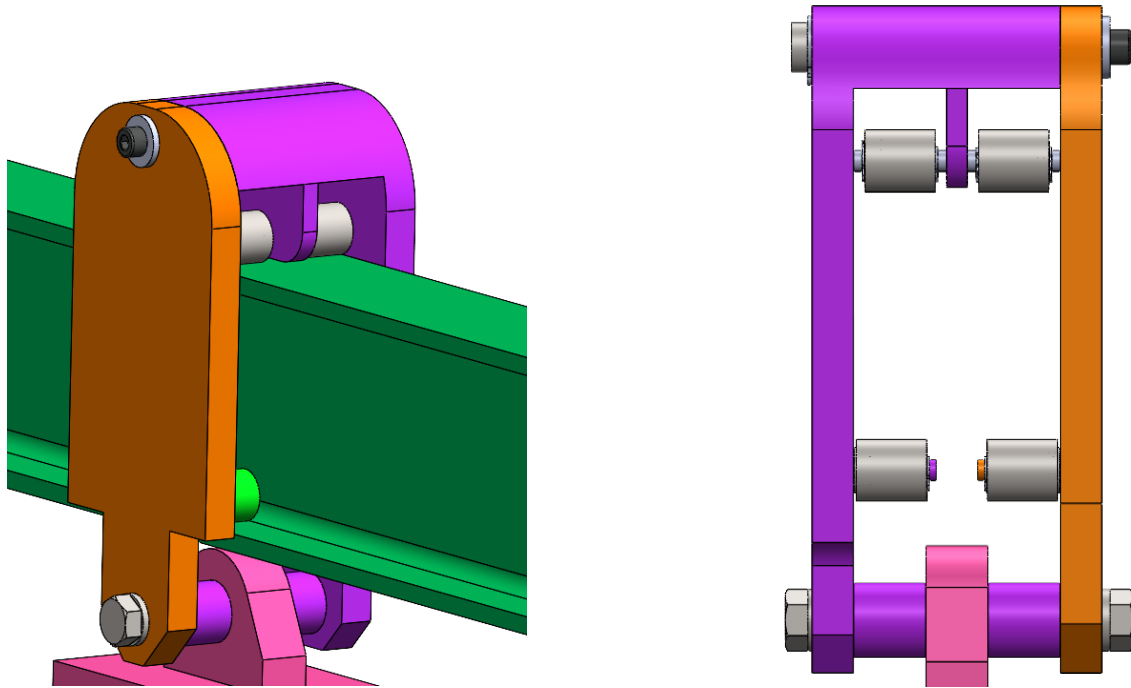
Vistas detalle del subconjunto del carrete (Fuente 26)
